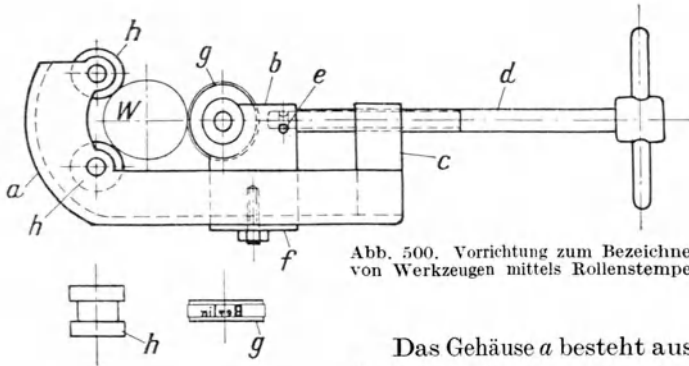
Vorrichtung zum Bezeichnen von Werkzeugen mittels Rollenstempel.
